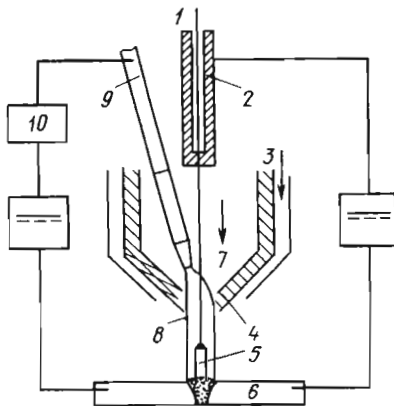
Схема процесса плазменной сварки с плавящимся электродом:
